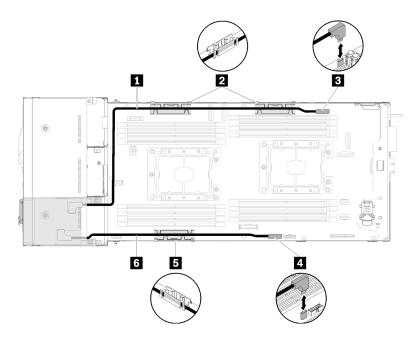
Roteamento de cabos do módulo breakout KVM direito
